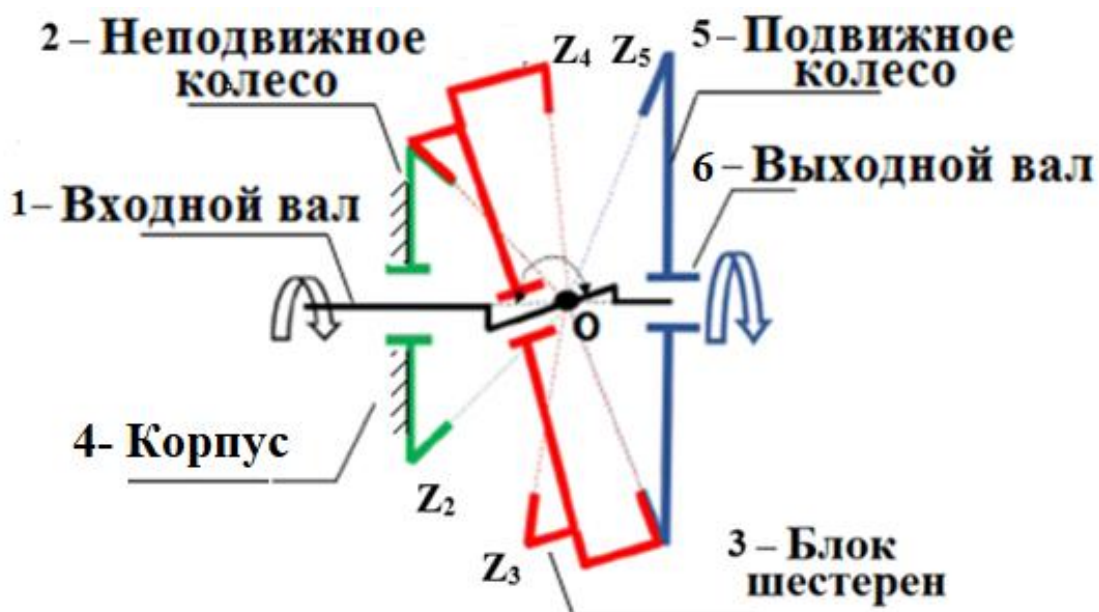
Структурная схема волнового торцевого кинематического редуктора
